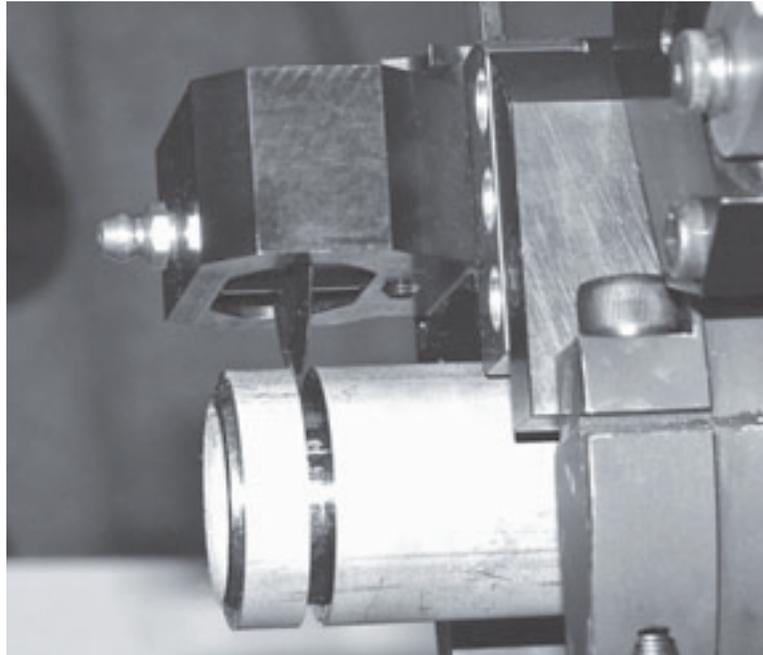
El casquillo se puede reutilizar después de ser removido del tubo.
